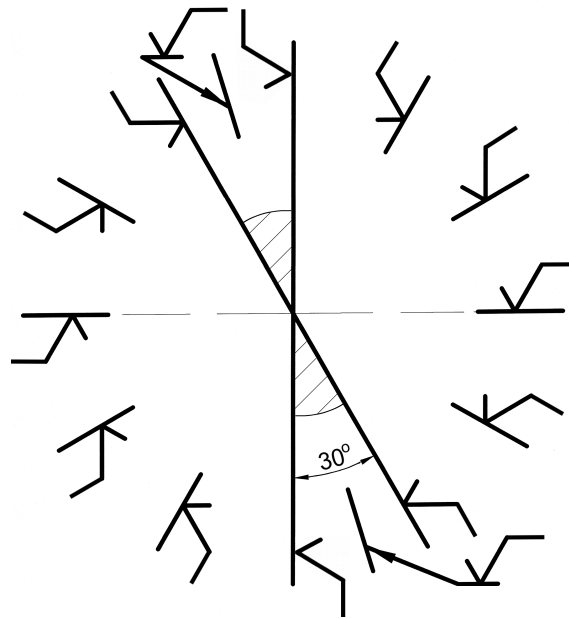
Примеры нанесения условных обозначений шероховатости
